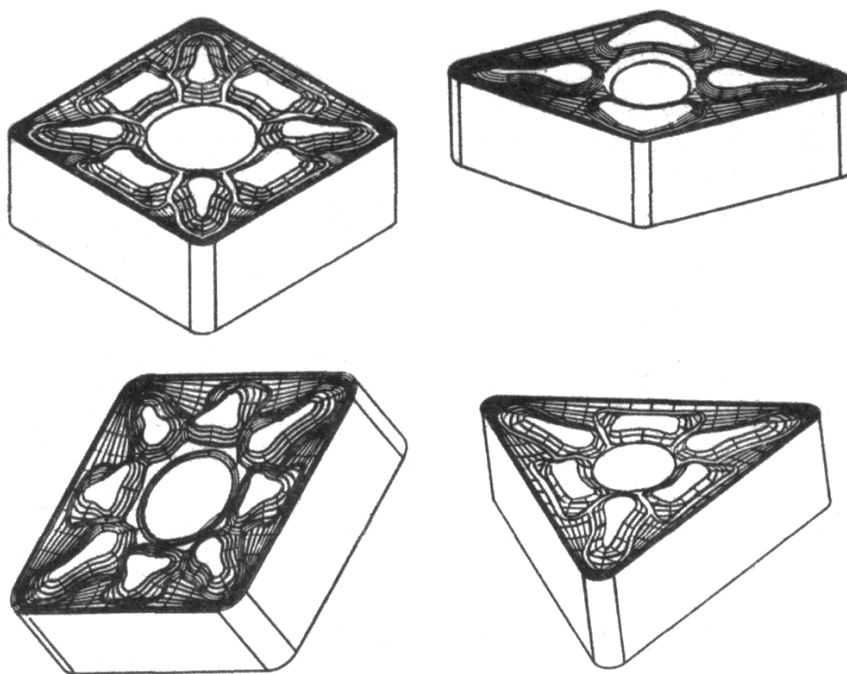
Пример конструкций пластин с однотипными стружколомающими поверхностями
